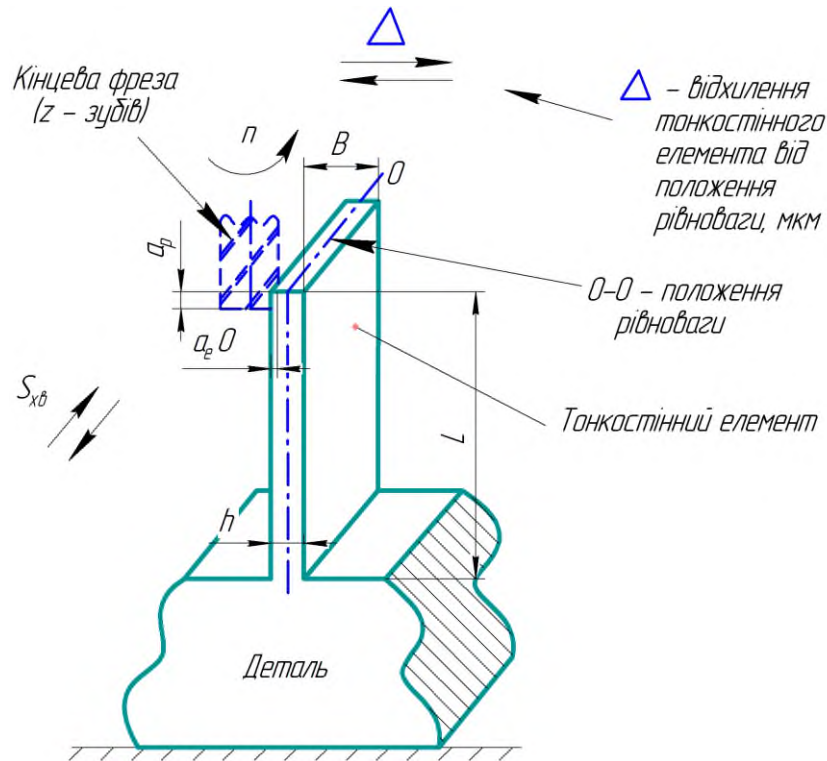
Принципова схема кінцевого фрезерування ТЕ [18]
